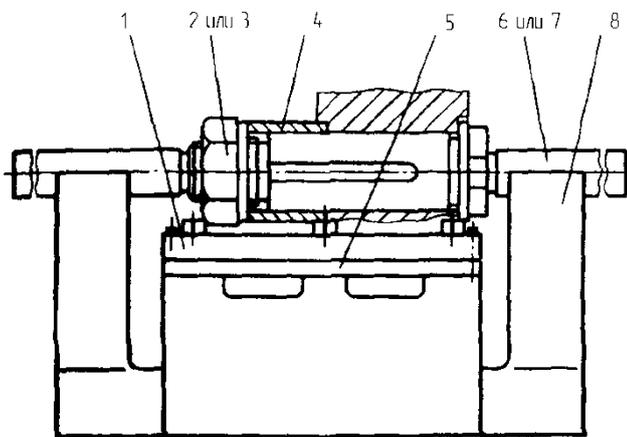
Приспособление для установки ножей сборных фрез ИП.23.000
